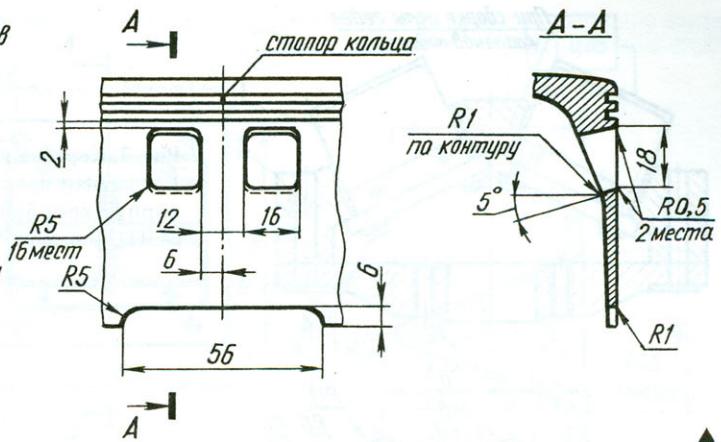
Доработанный поршень (поверхность поршня развернута в плоскости чертежа).
